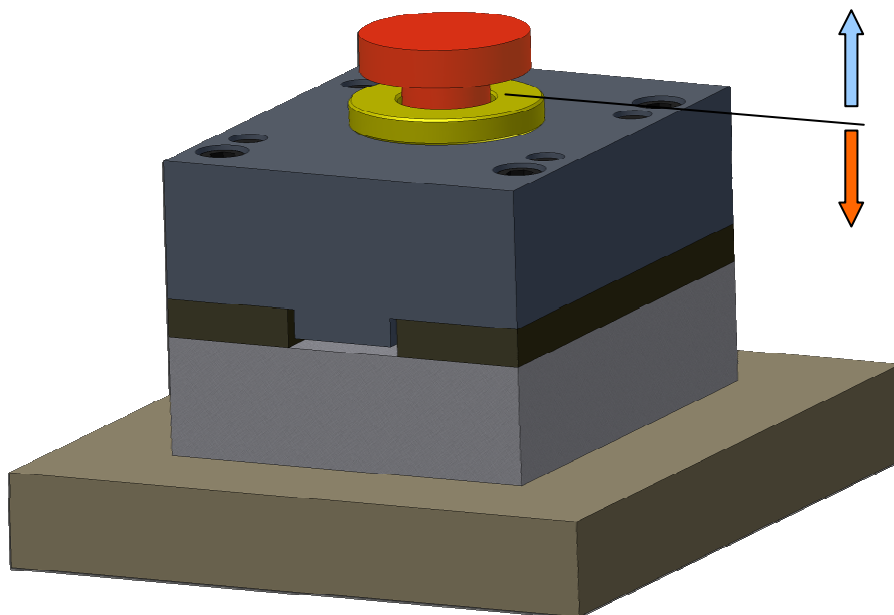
Vylisované zahloubení ve zkušebním vzorku
